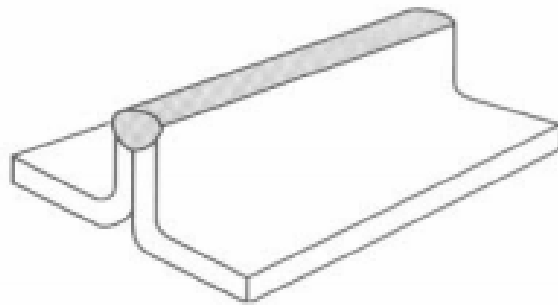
Soldadura en borde a tope con componentes curvos.
